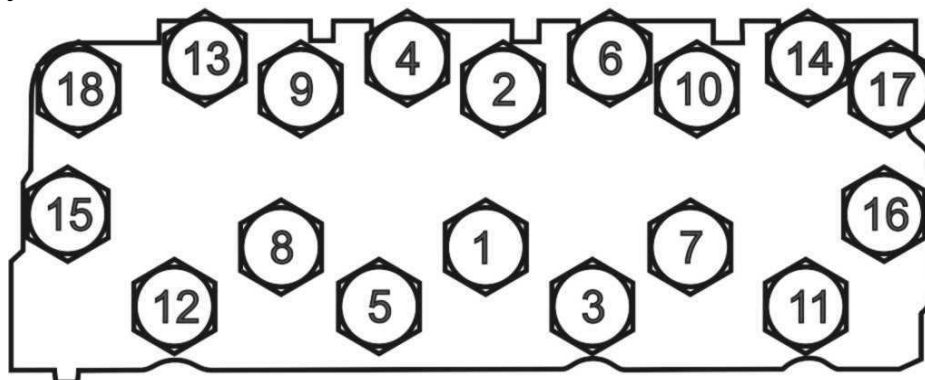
Порядок подтяжки гаек крепления головок цилиндров
